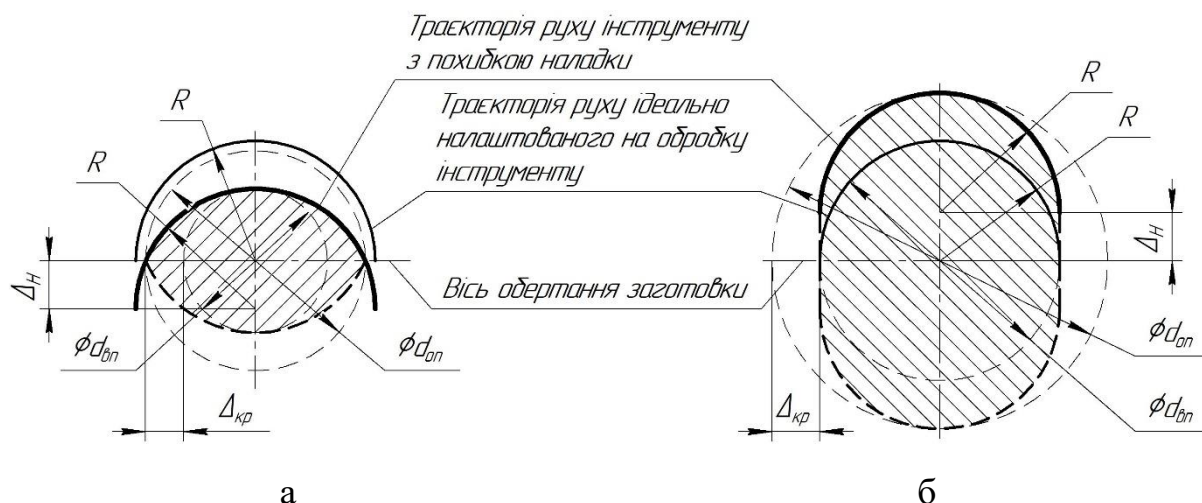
Спотворення форми деталі при радіальному зміщенні інструменту до (а) і від осі (б) обертання заготовки:
